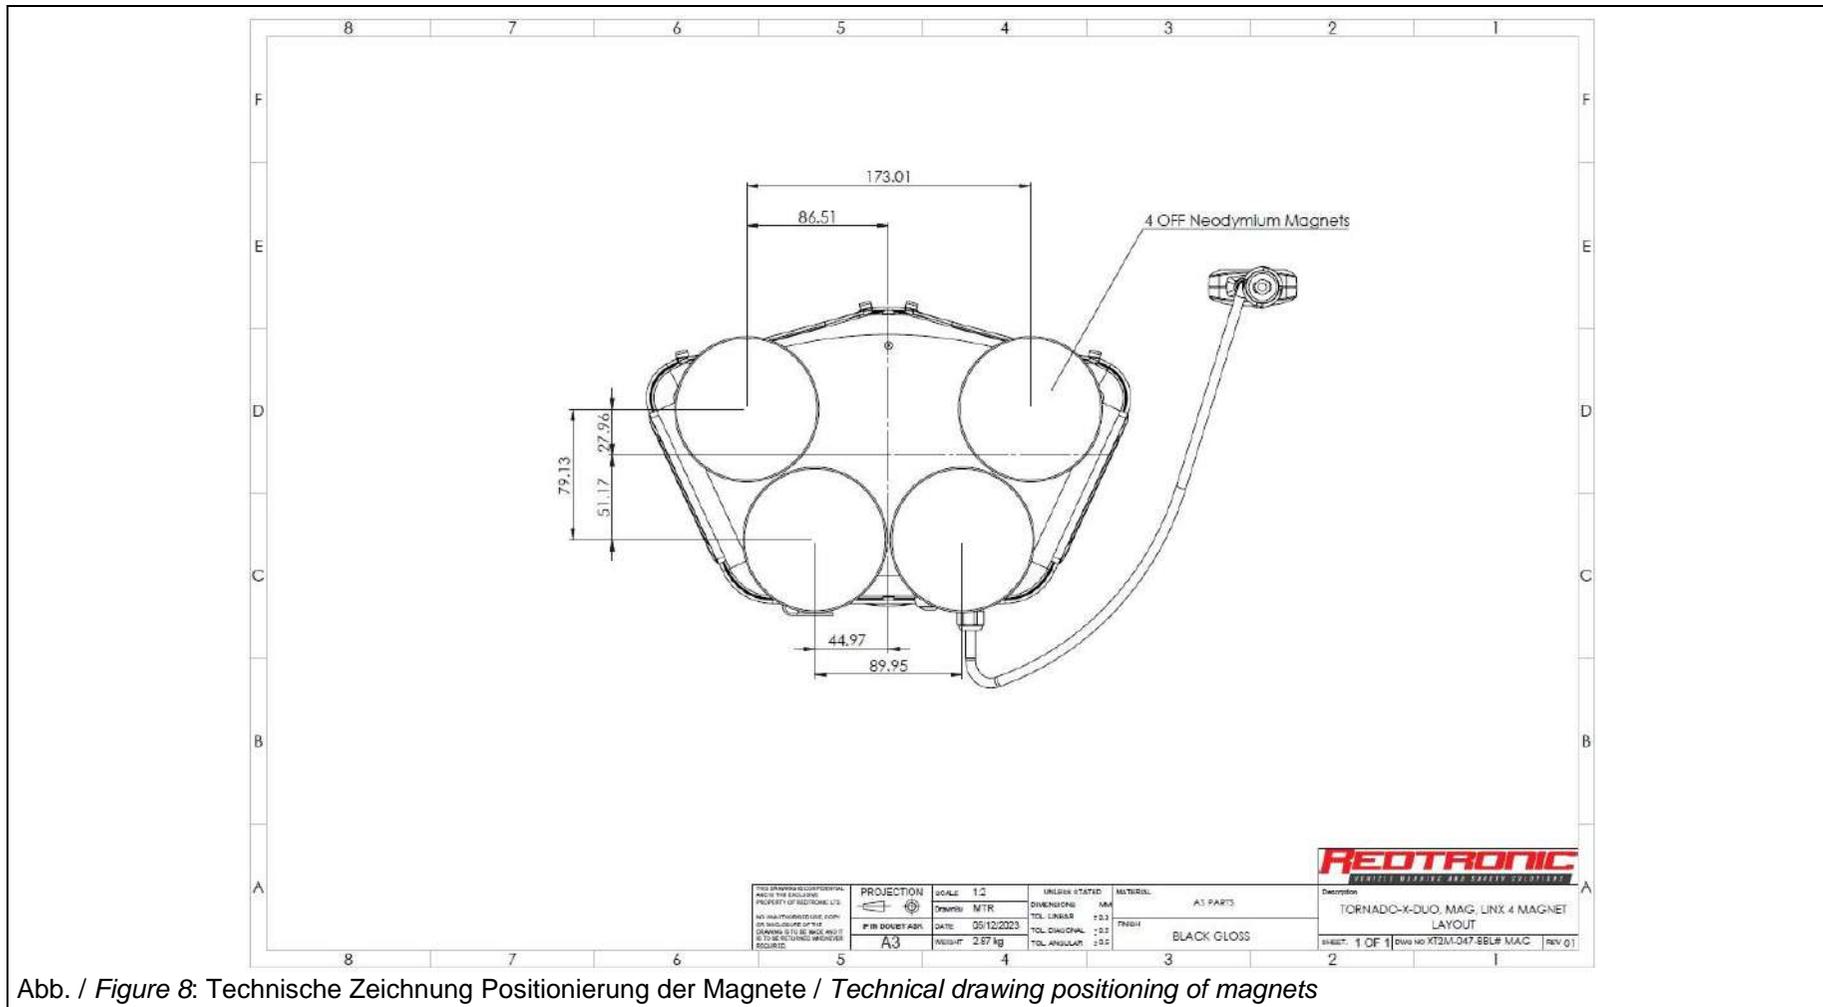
Technische Zeichnung Positionierung der Magnete / Technical drawing positioning of magnets
